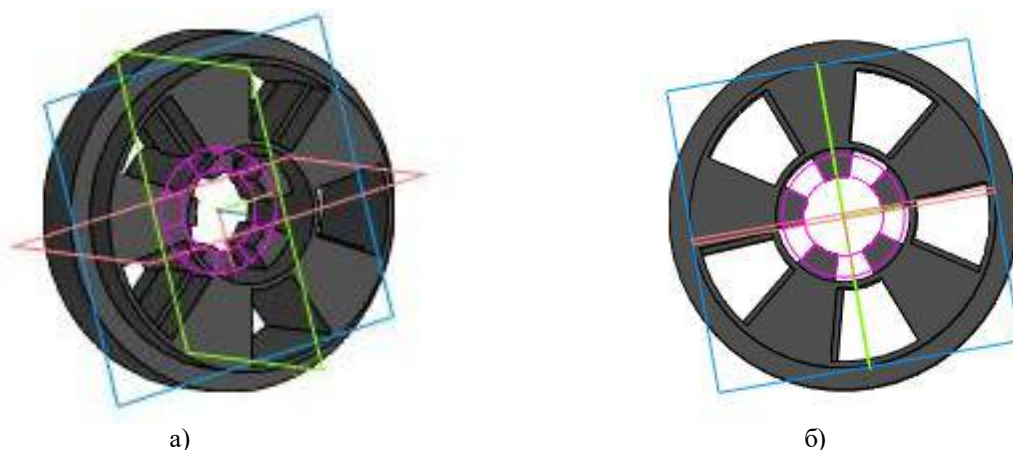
Вид ступицы: а) – под углом; б) - сверху
